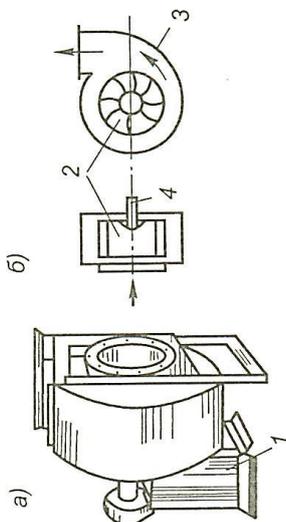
а) Общий вид; б) схема устройства центробежного вентилятора
